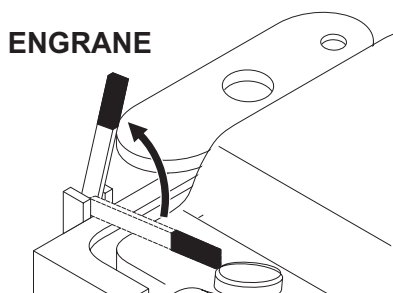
Palanca de transmisión engrane/desengrane (posición de engrane)
